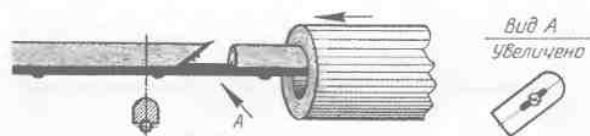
Приспособление для расширения и обработки цилиндрической полости, обеспечивающее выход стружки
